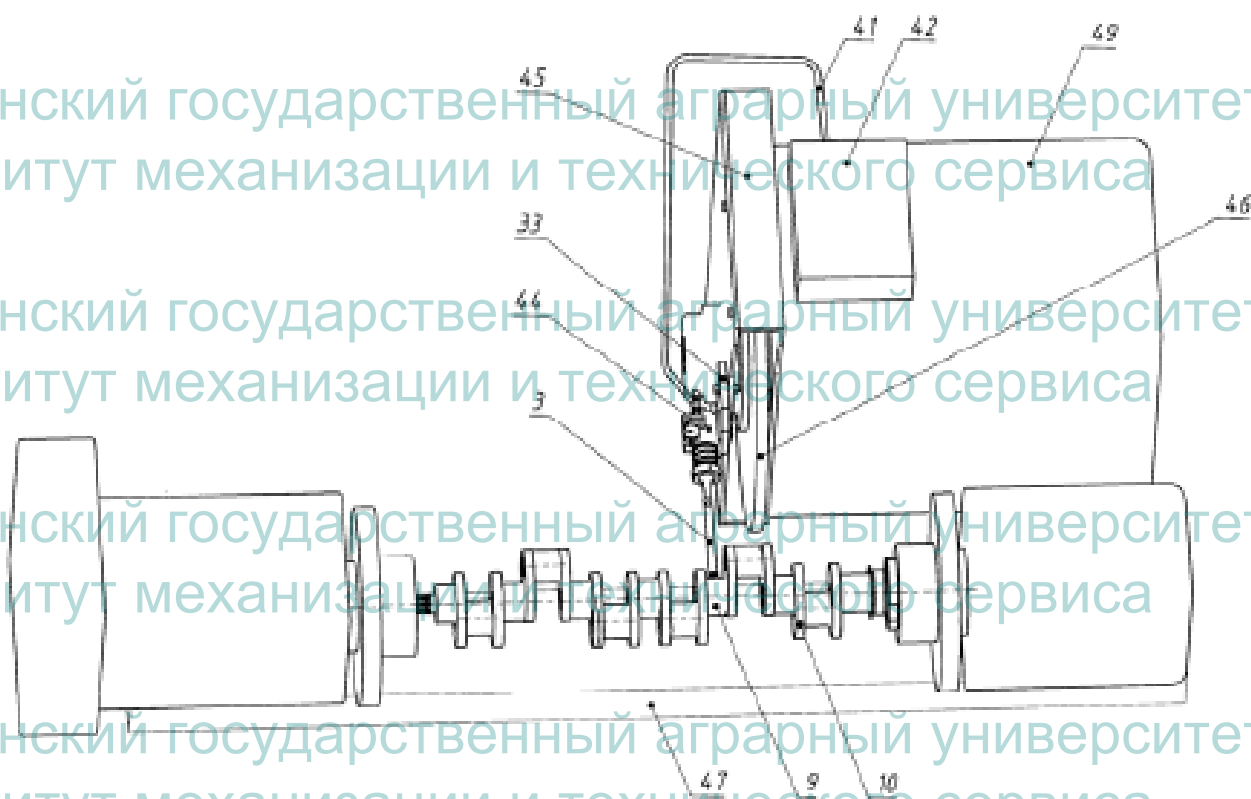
Схема ультразвуковой обработки коленчатого вала
